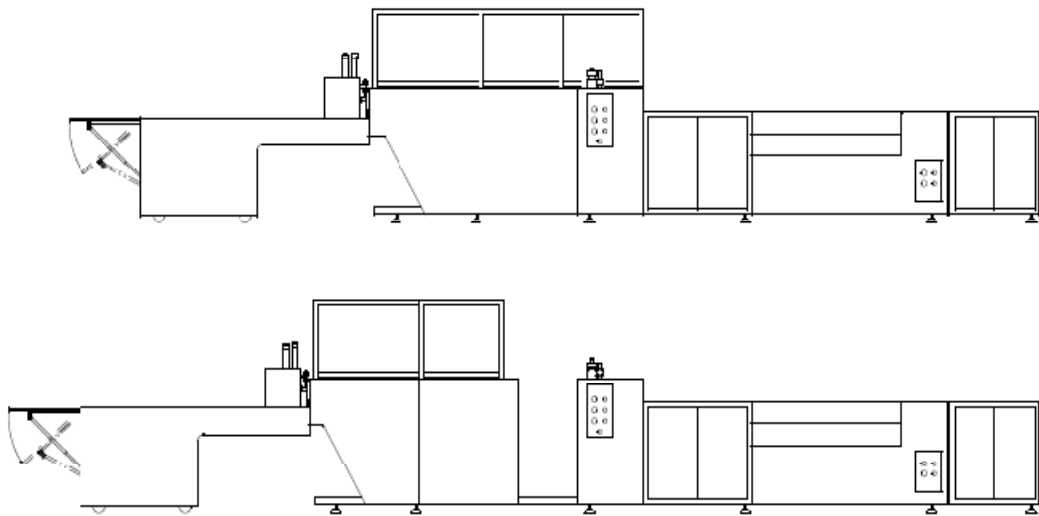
Mesa próxima y mesa alejada de la soldadora.
